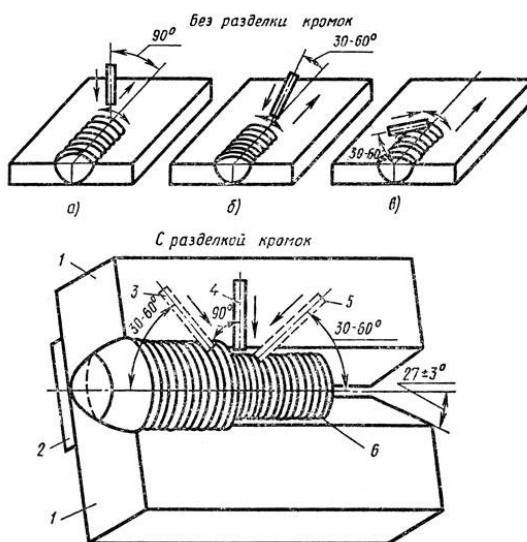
Техника сварки стыкового соединения: а - вертикально расположенным электродом, б - углом назад, в - углом вперед; 1 - свариваемые пластины, 2 - подкладка, 3 - положение электрода углом вперед, 4 - вертикально расположенным электродом, 5 - положение электрода углом назад, б - корневой шов
